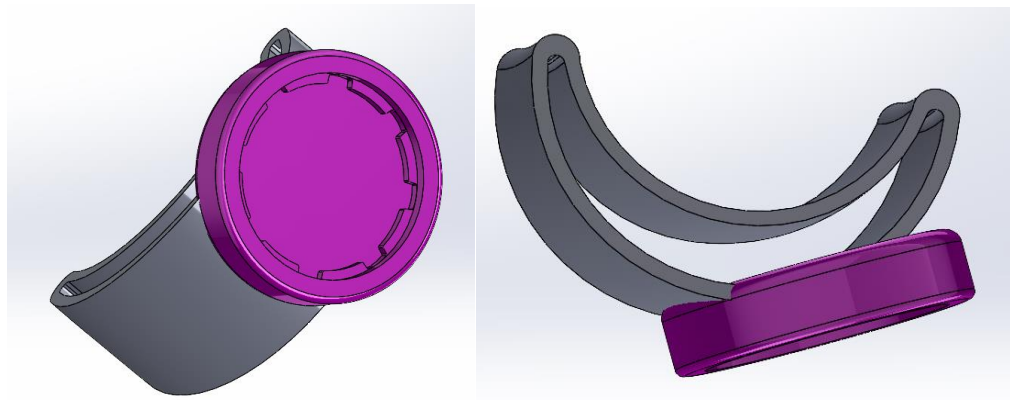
Soporte cierre BOA Bambú Propia autor.
